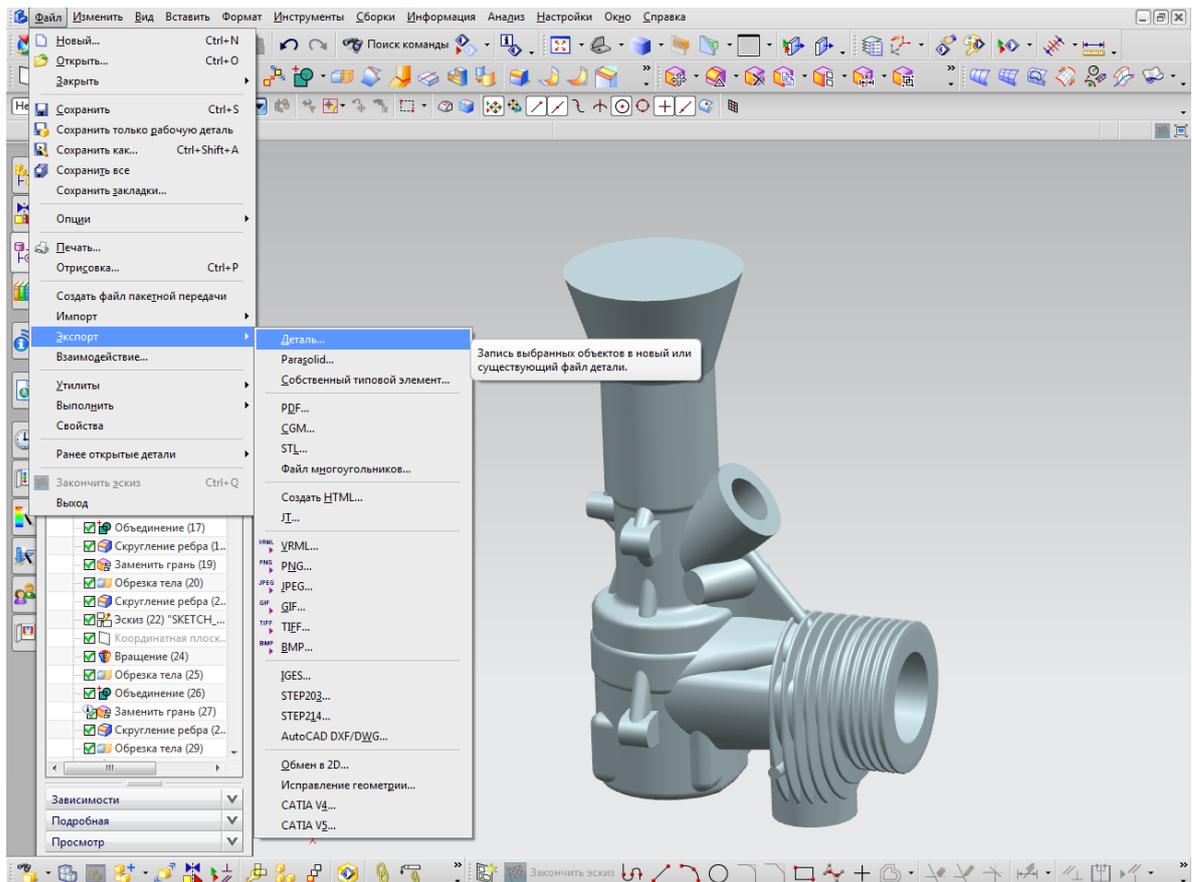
Экспорт 3D-модели отливки в формат Parasolid
